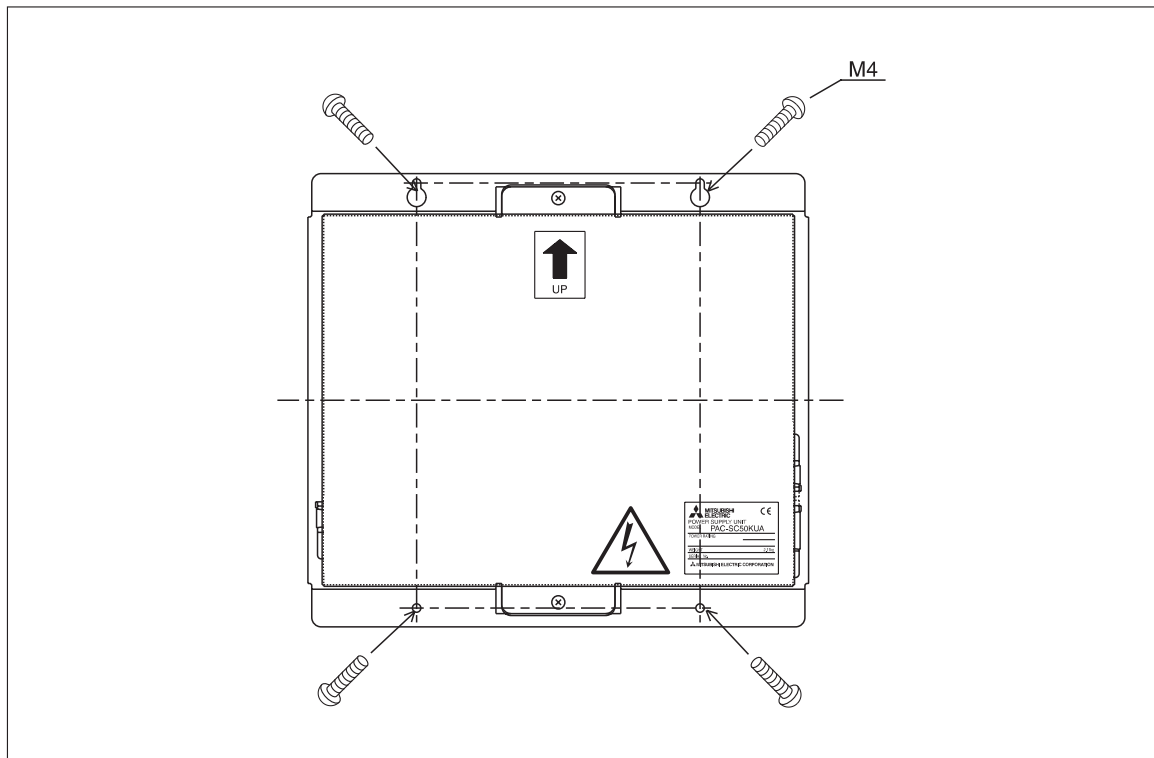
Position der Befestigungsschrauben und -bohrungen
